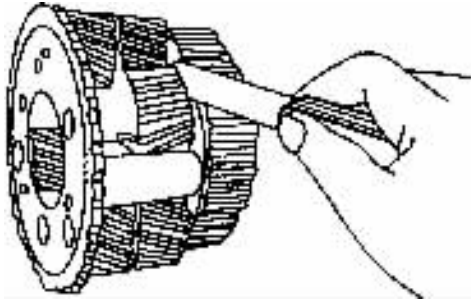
用塞尺检查行星齿轮与行星轮架的间隙
